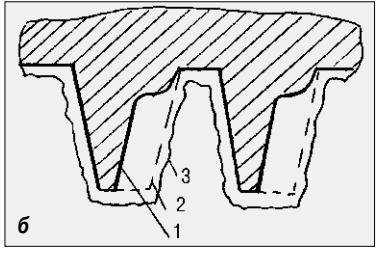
Внешний вид восстановленных и механически обработанных секторов зубчатого венца шаровой мельницы
